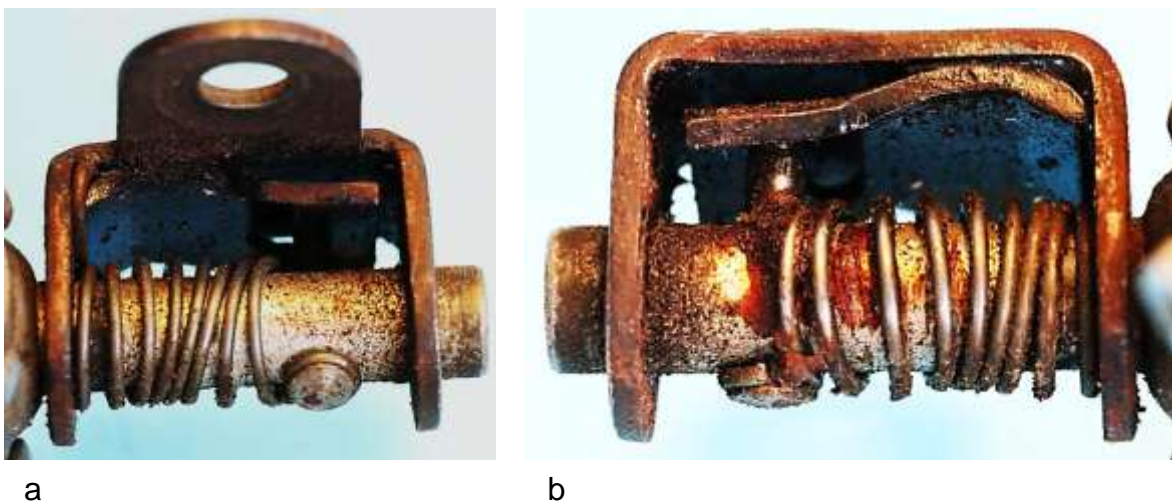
Kippvorrichtung: a) Ansicht mit dem Halterarm, b) Ansicht von oben mit der Position des Kulissenblechs
